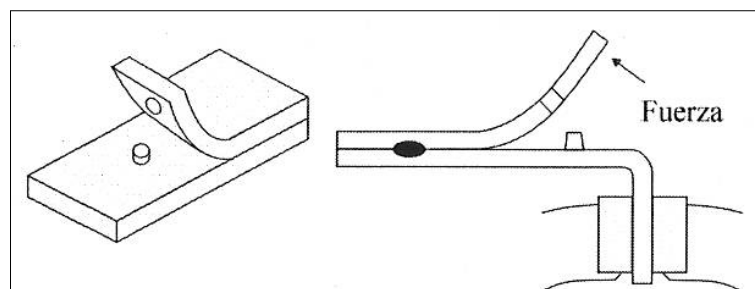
Detalle de un ensayo destructivo realizado a dos hojas metálicas soldadas por resistencia.
